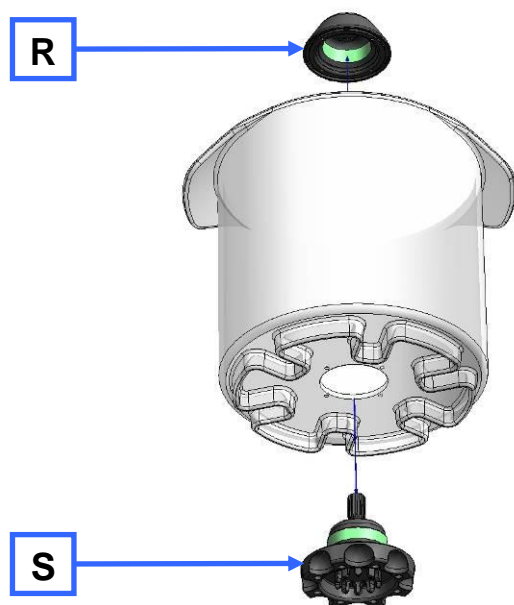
Vue à proximité pour le démontage des bols de broyage
